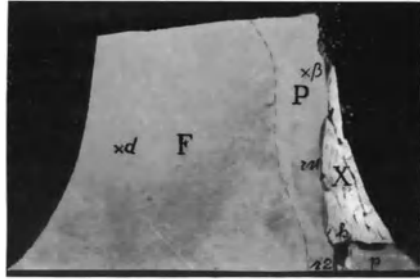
Gebrochener Propellerflügel mit angeschmolzenem Material.
